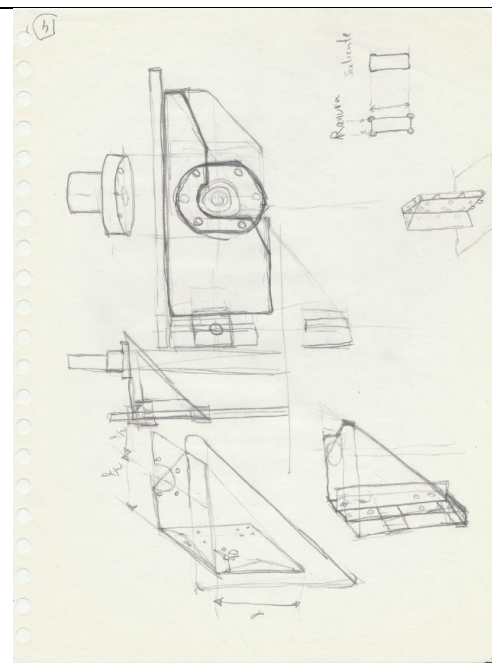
Bosquejo detalle pieza del elevador de altura del cabezal que se atornilla a la tuerca del sinfín.
